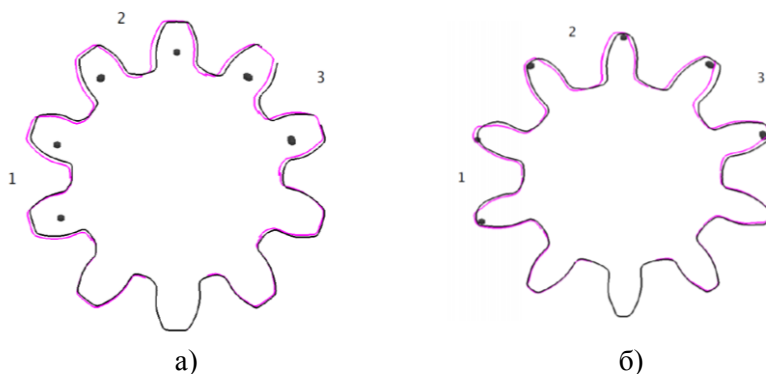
Профили сечений колеса, подверженного перед лазерной обработкой объемной закалке и отпуску. Пары зубьев, закаленных при перемещении луча лазера со скоростью:
